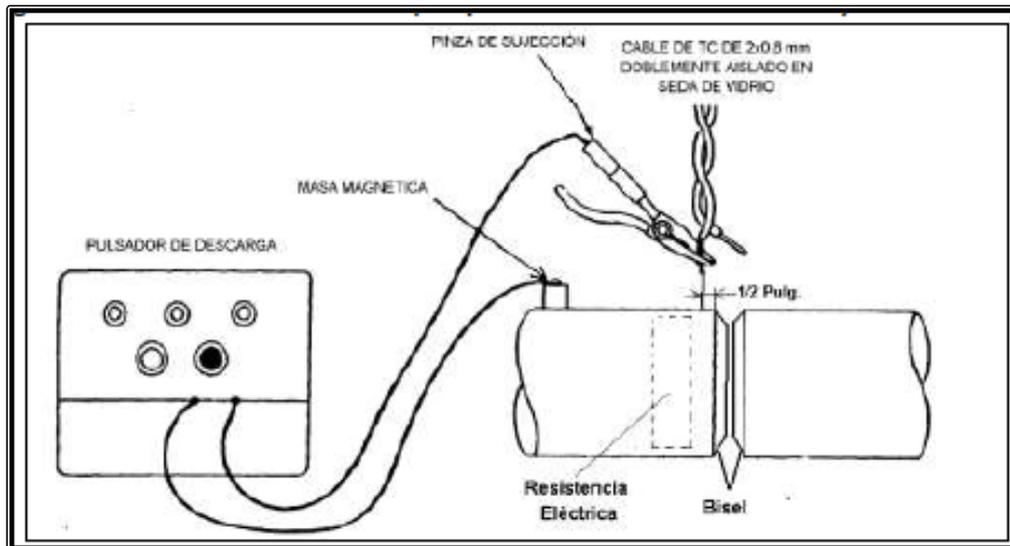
INSTALACIÓN DE CABLE TERMOCUPLAS PARA TRATAMIENTO TÉRMICO PRE Y POST SOLDADURA.
